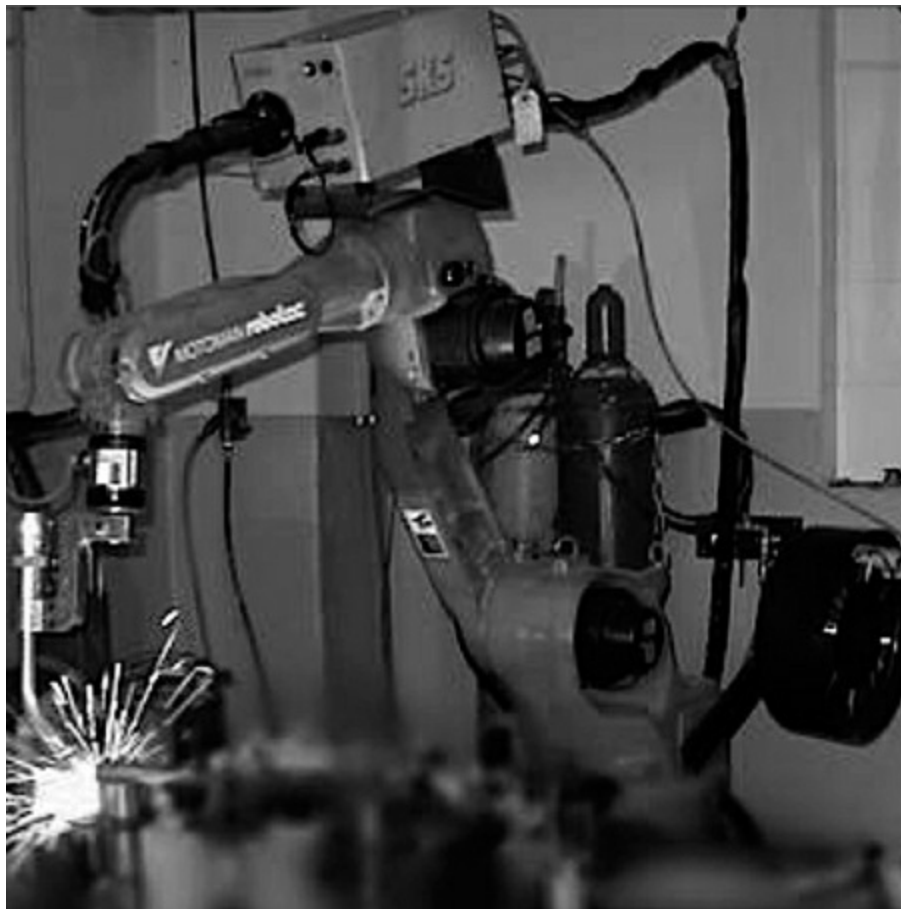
Robot equipado y programado para realizar operaciones de soldadura.
